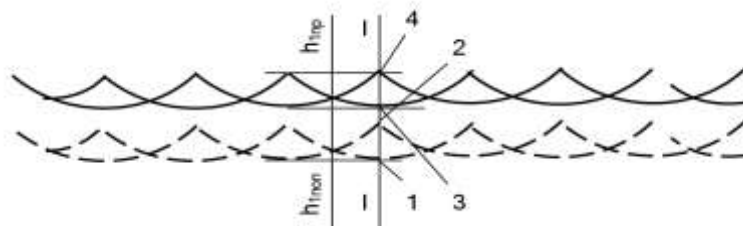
Формування поверхні зубчастого колеса після обробки ріжучою крайкою фрези по всій довжині асиметричного зуба
